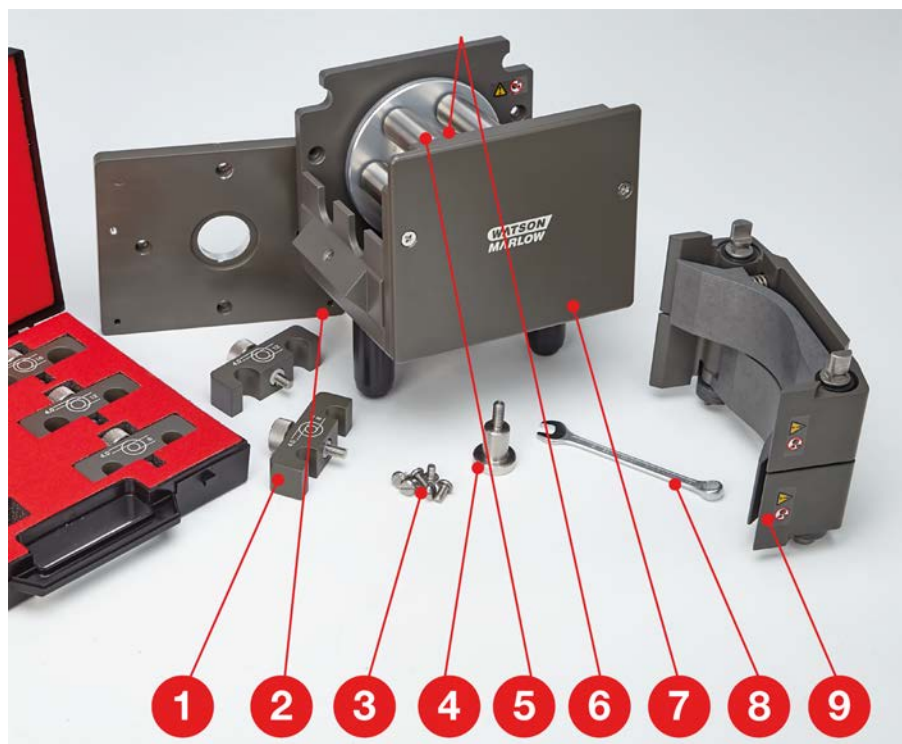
Peças de reposição para os cabeçotes 620L e 620LG
